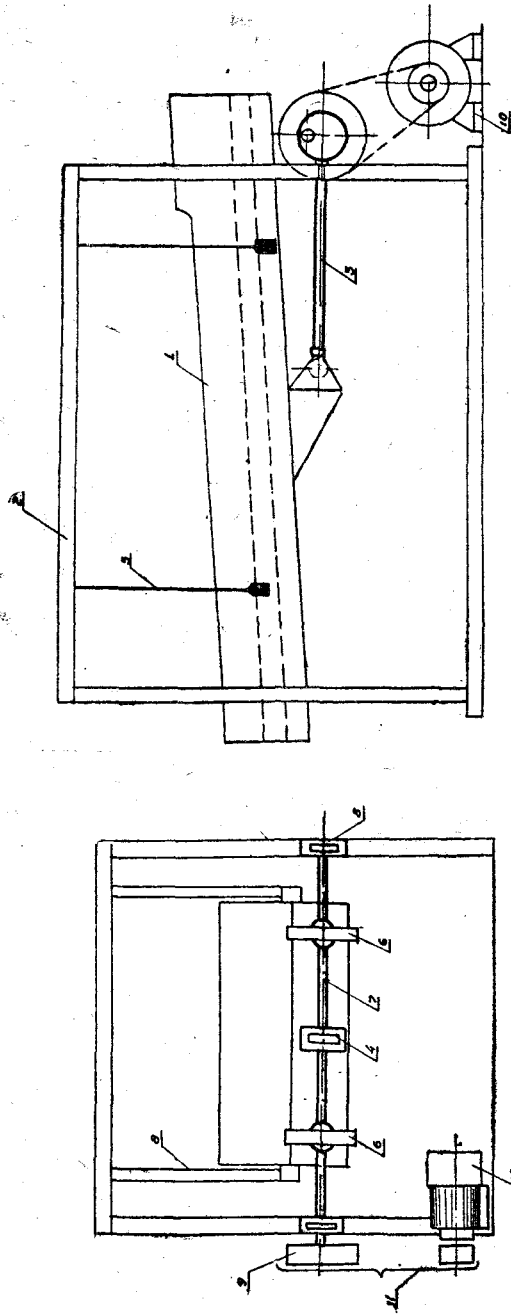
Схема просеивающего устройства с эксцентриковым приводом:
